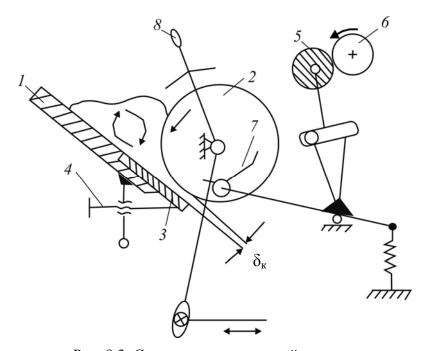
Схема краскоподающей группы: 1 – красочный ящик; 2 – дуктор; 3 – красочный нож; 4 – винты; 5 – передаточный валик; 6 – раскатной цилиндр; 7 – кулачок; 8 – ручка
